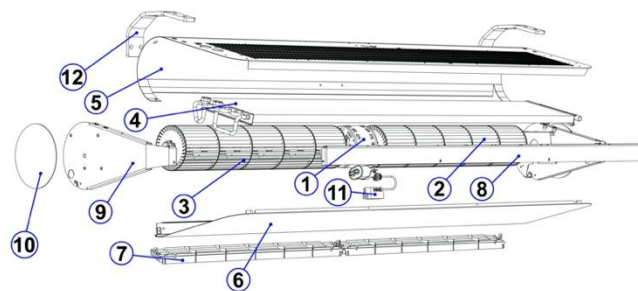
CONSTRUCȚIE SLIM N/W.
